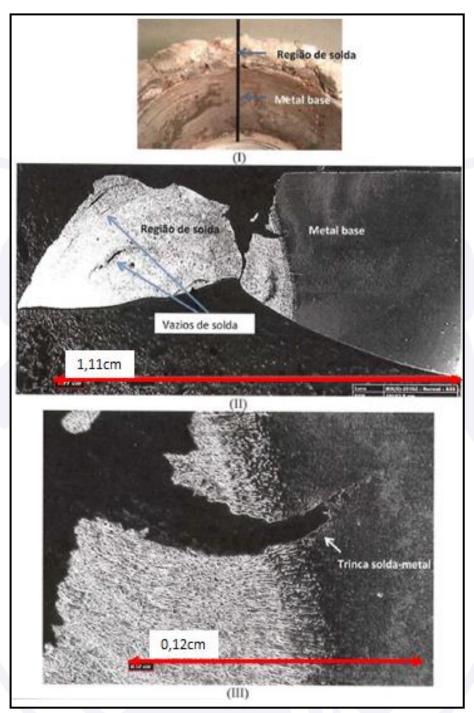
Em (I) detalhe da região de solda e de metal base. Em (II) pode-se observar a seção metalográfica da solda e o metal base. A região de solda apresenta vazios devido ao processo de soldagem ineficiente. Em (III) pode-se observar uma trinca originada na região de solda e com avanço no metal base.
